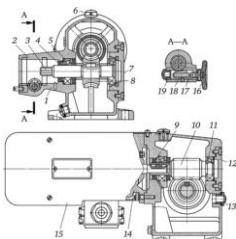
Малогабаритный привод УММ-ПР: 1 — корпус; 2 — горловина; 3 — вал; 4,9 — манжета; 5,11 — роликподшипник кониче-
